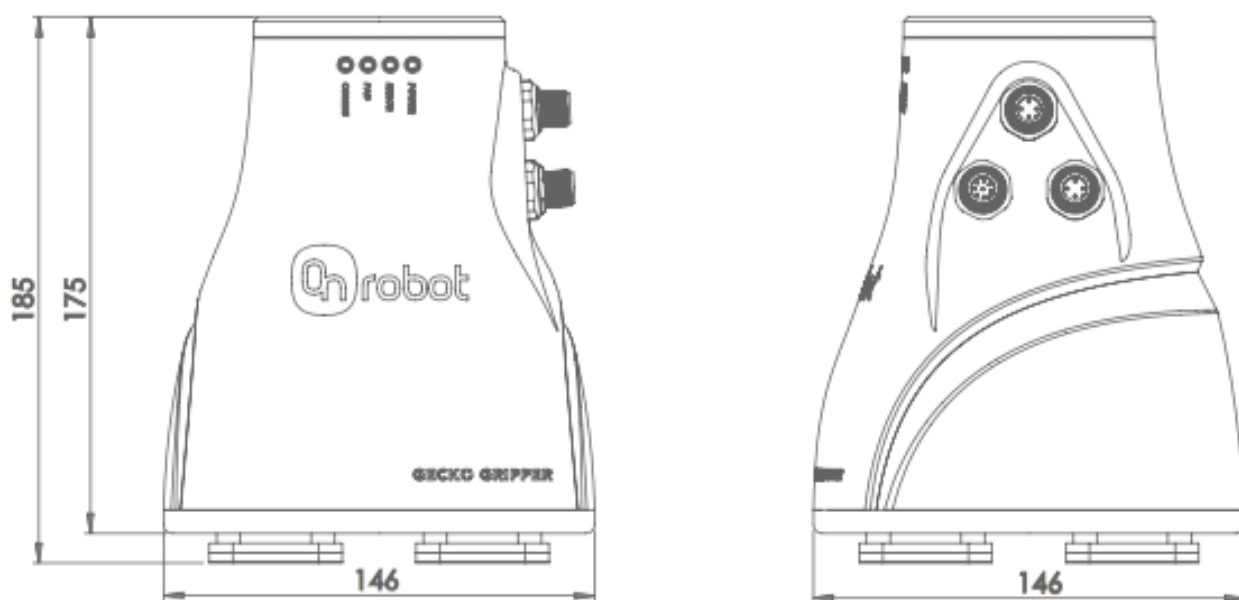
Размеры передней и боковой части захватного устройства Gecko
